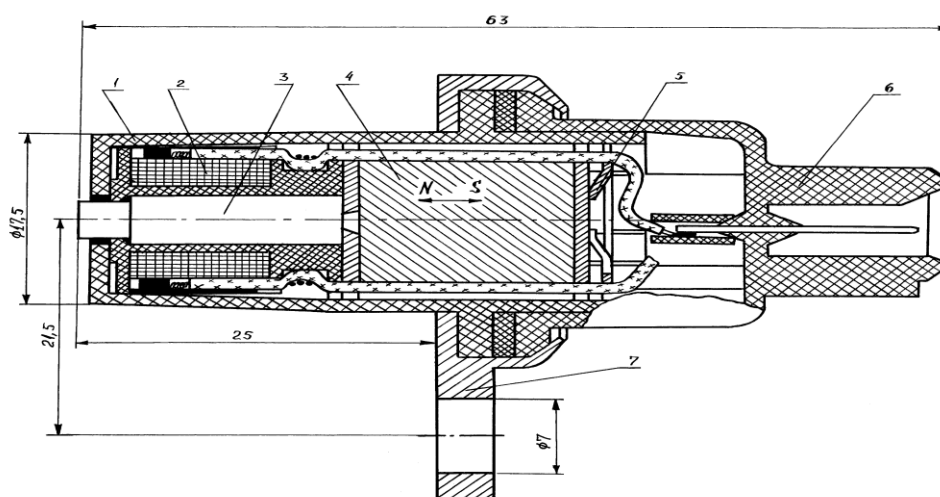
Конструкция типичного индуктивного датчика перемещения: 1 – корпус; 2 – катушка; 3 – сердечник; 4 – постоянный магнит из феррита бария; 5 – кольцо пружинное; 6 – разъем датчика со штекерами; 7 – фланец крепления датчика
